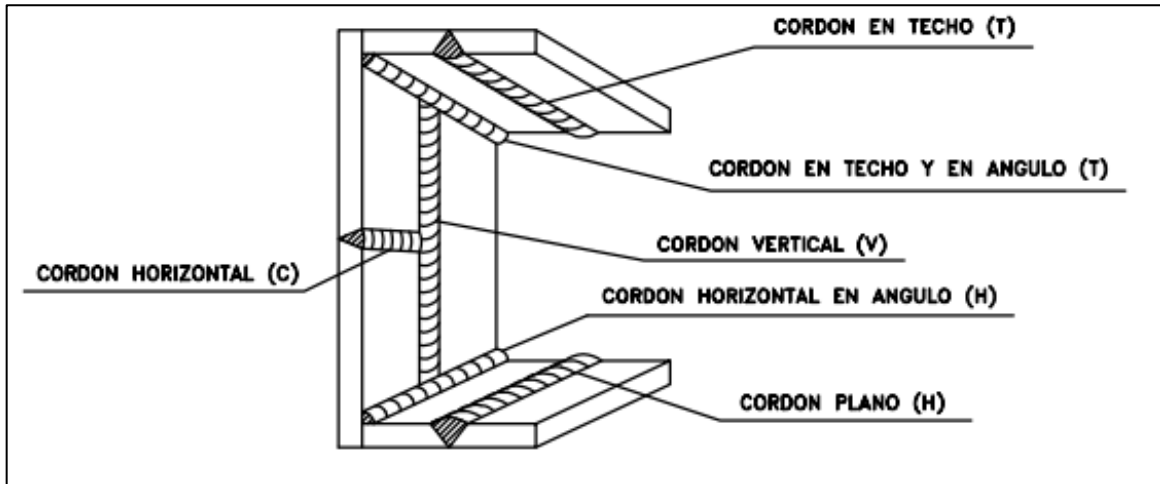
Clasificación de cordones de soldadura según su posición. Fuente: UCLM Web.
